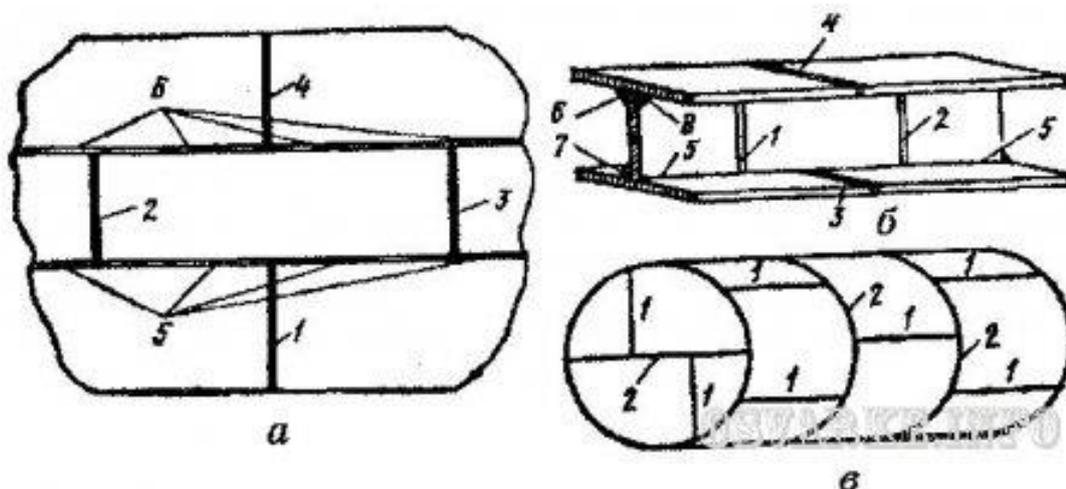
Последовательность наложения швов (1-8) при сварке: а - полотна из отдельных листов; б - двутавровой балки; в - цилиндрического сосуда
